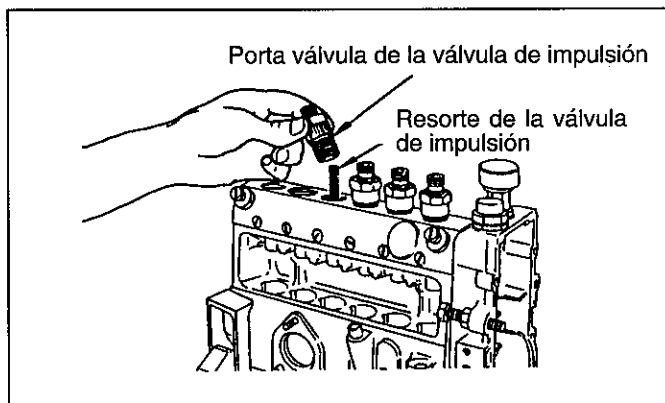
Desmontaje del porta válvula de la válvula de impulsión
